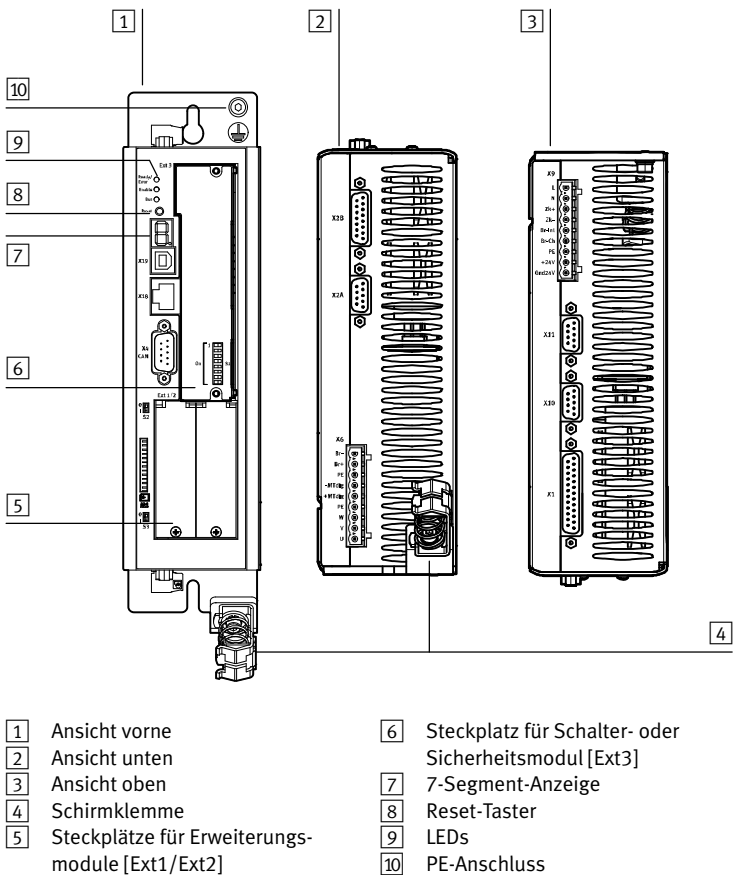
Motorcontroller CMMP-AS-...-M3 (Beispiel CMMP-AS-...-C2-3A-M3)
